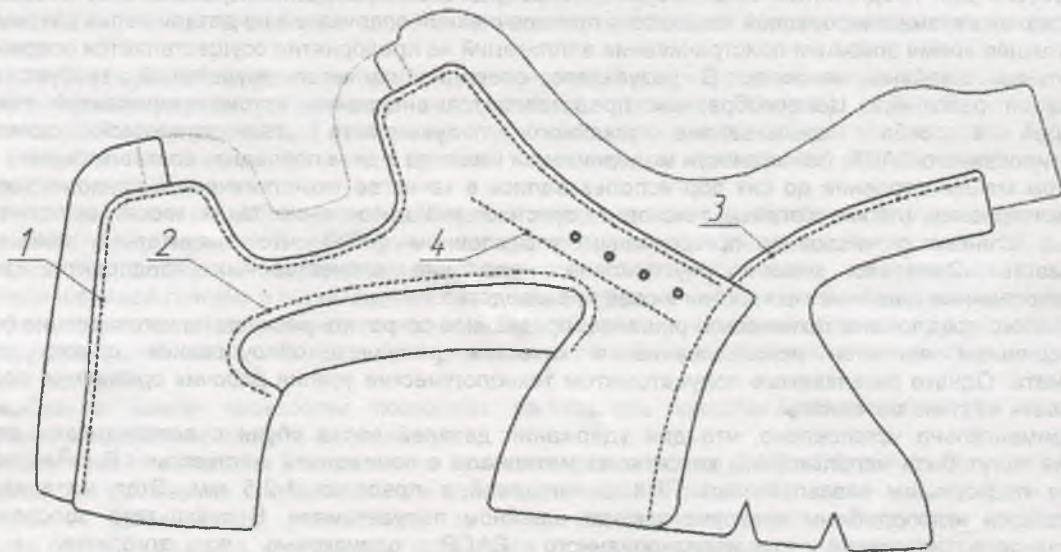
Контур детали верха обуви и соединительных строчек
